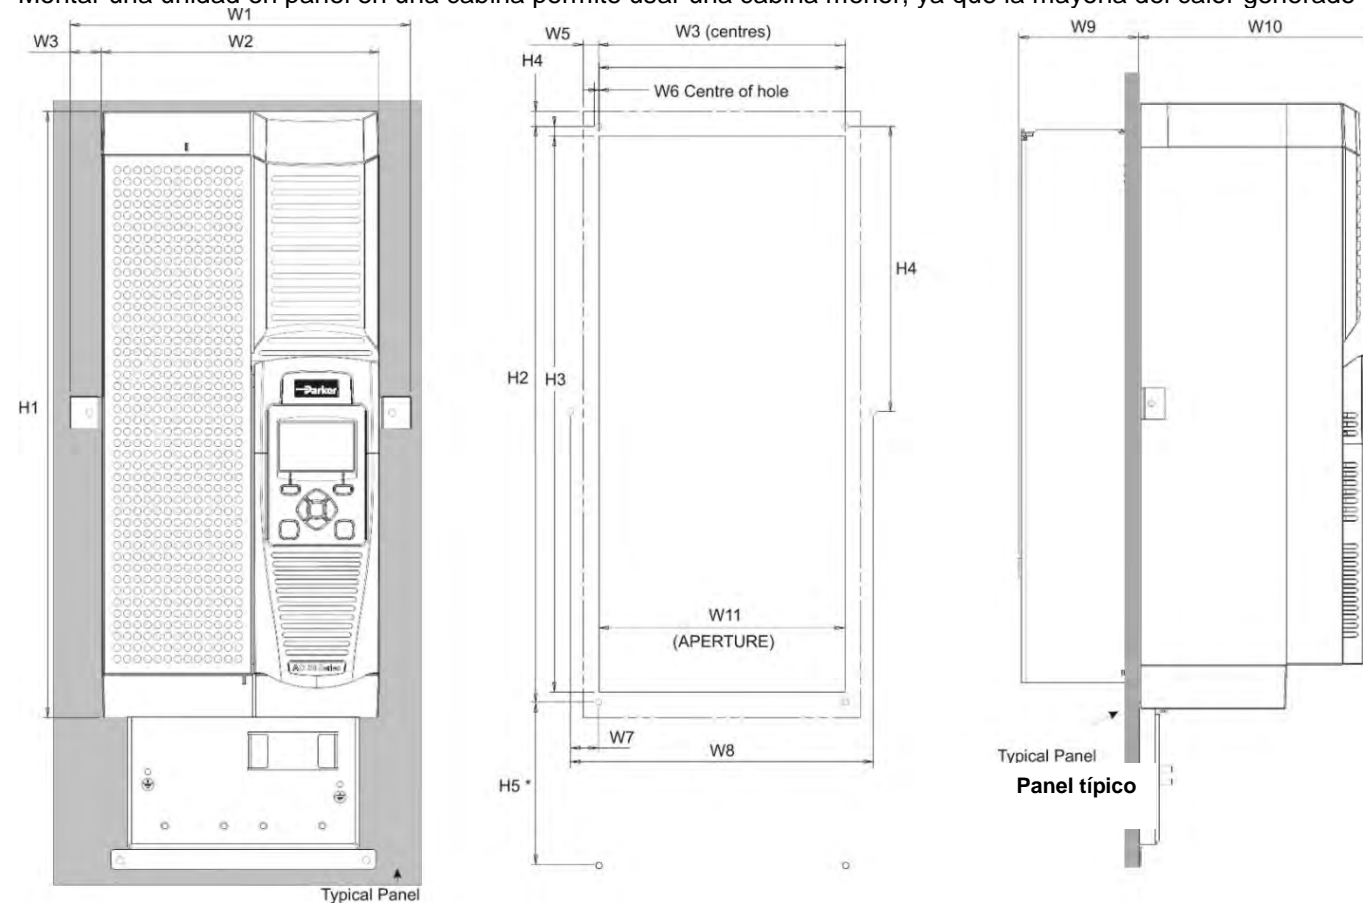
5 Dimensiones mecánicas de la unidad AC30 de montaje en panel - Tamaños F, G
